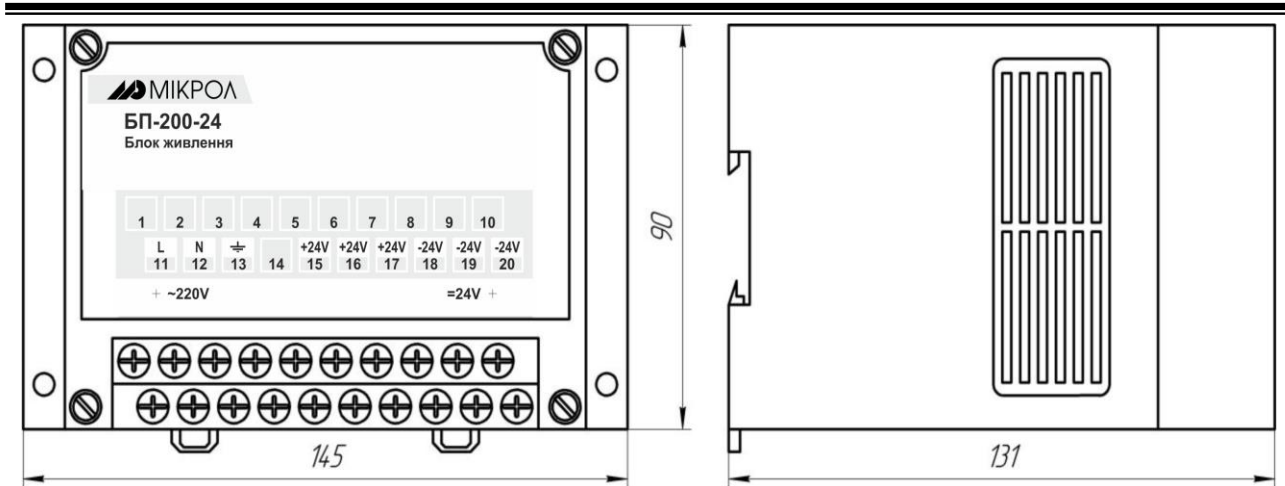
Внешний вид и габаритные размеры БП-200-24
